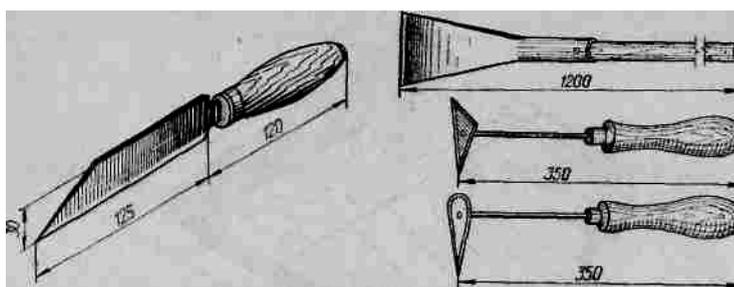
Ніж металевий Рис. 24.5. Скребачки металеві
